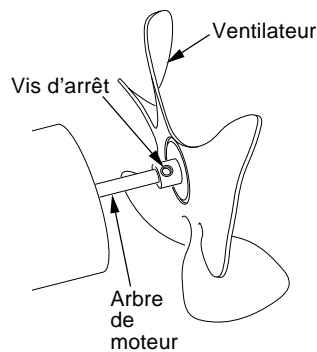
Emplacement du ventilateur, de l'arbre moteur et des vis d'arrêt
